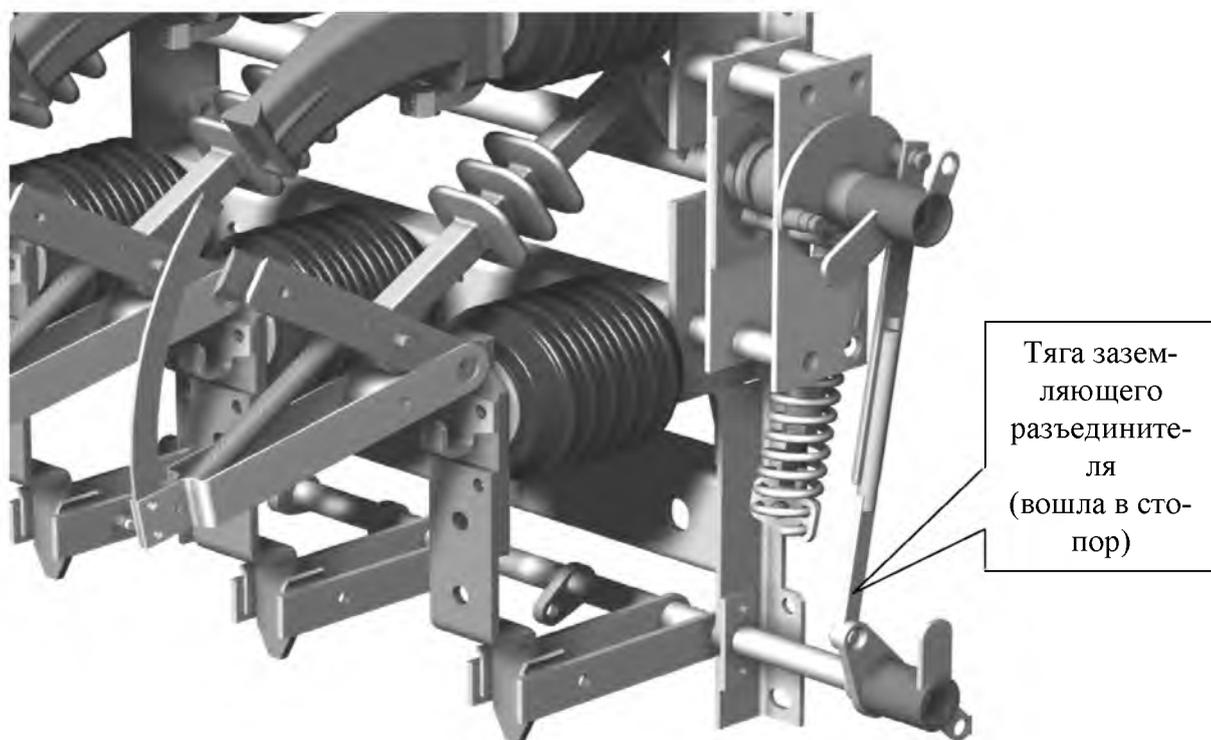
Блокировка выключателя нагрузки и заземляющего разъединителя (выключатель нагрузки отключен, заземляющий разъединитель включен).
